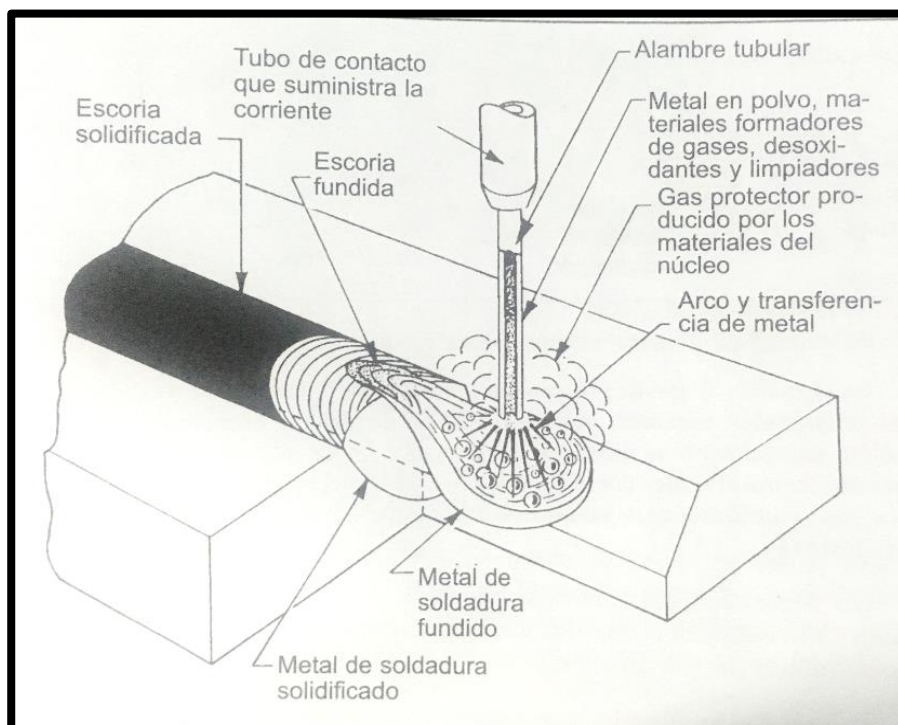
Proceso con alambre tubular autoprotegido. Tomada del Manual del soldador
